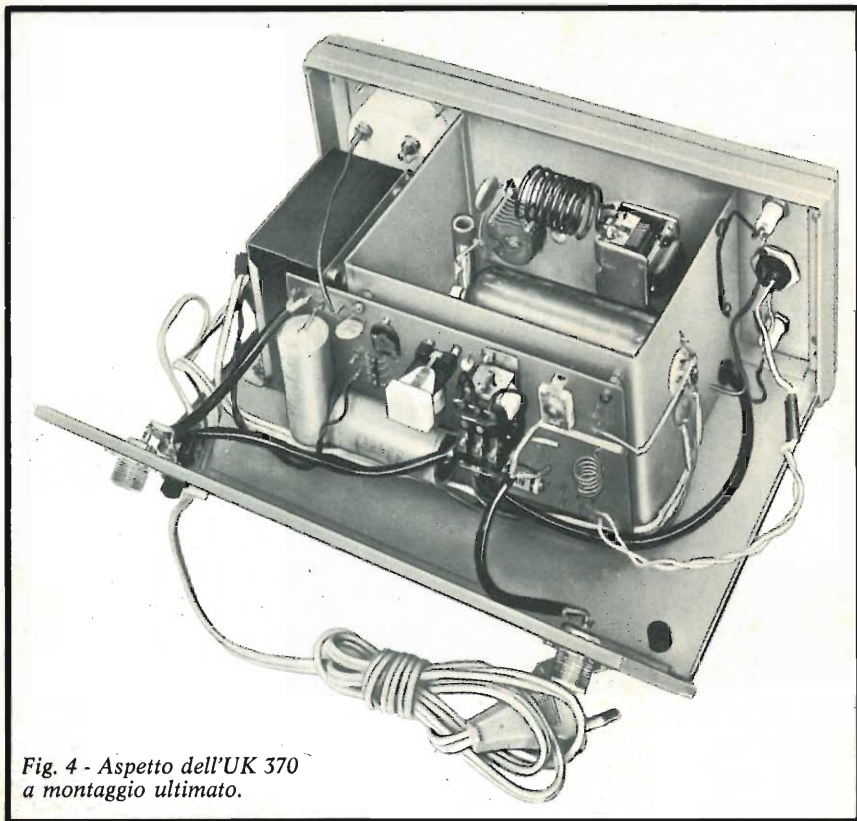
Aspetto dell'UK 370 a montaggio ultimato.
